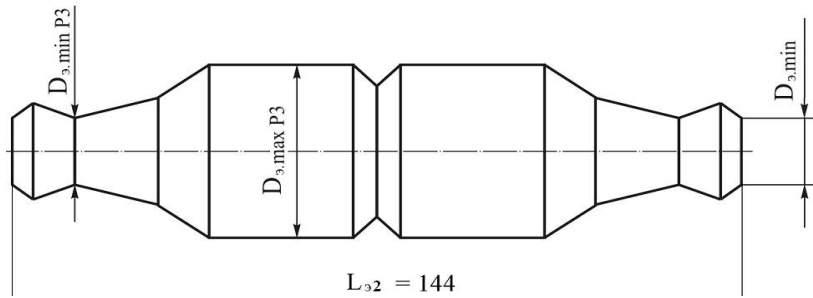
Эскиз формы развертки расчетной заготовки для спаренной штамповки двух поволоков «рым - болт»
